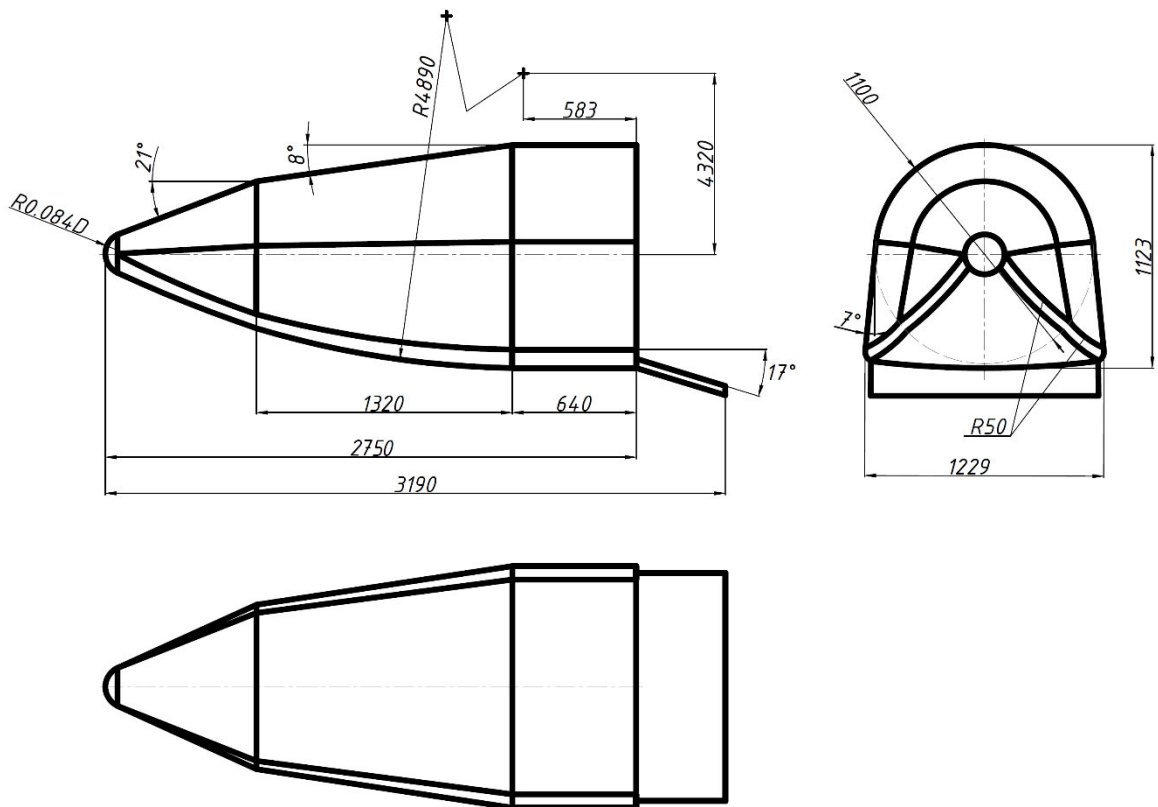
Теоретический чертеж аппарата класса «несущий корпус» с кормовым щитком и $D = 1.1\text{м}$
